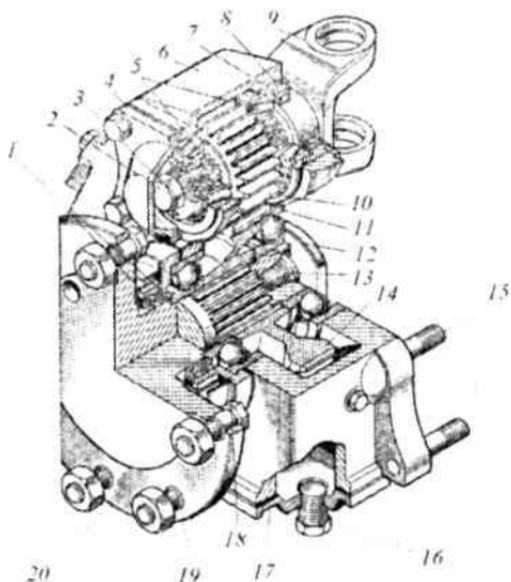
Конечная передача: 1, 8 – манжеты; 2, 13, 19 – болты; 3, 12 – стопорные шайбы; 4 – крышка; 5 – роликоподшипник; 6 – корпус; 7 – стакан подшипника; 9 – вилка ведущей шестерни; 10 – ведущая шестерня; 11 – шарикоподшипник; 14 – ведомая шестерня; 15 – шпилька; 16 – пробка; 17 – поддон; 18 – корпус манжеты; 20 – полуось
